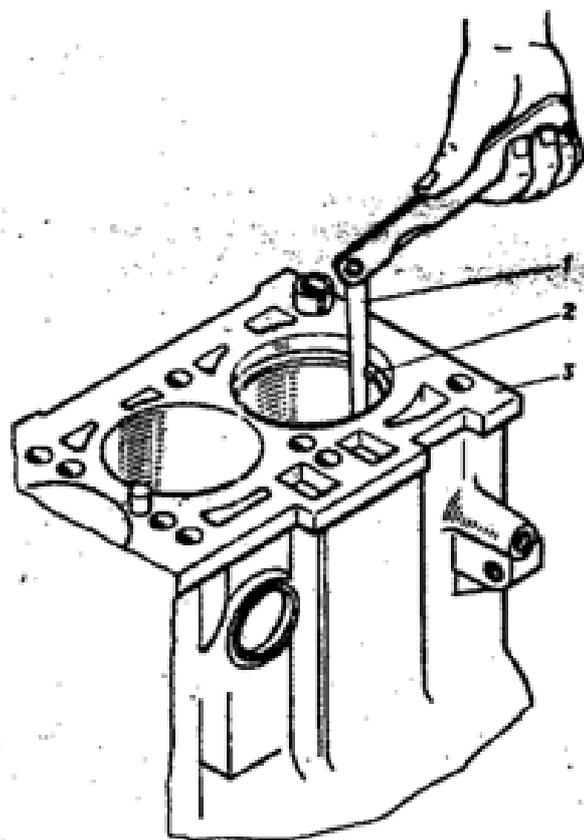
Проверка зазора в замке поршневого кольца, установленного в цилиндр: 1 - щуп; 2 - поршневое кольцо; 3 - блок цилиндров
